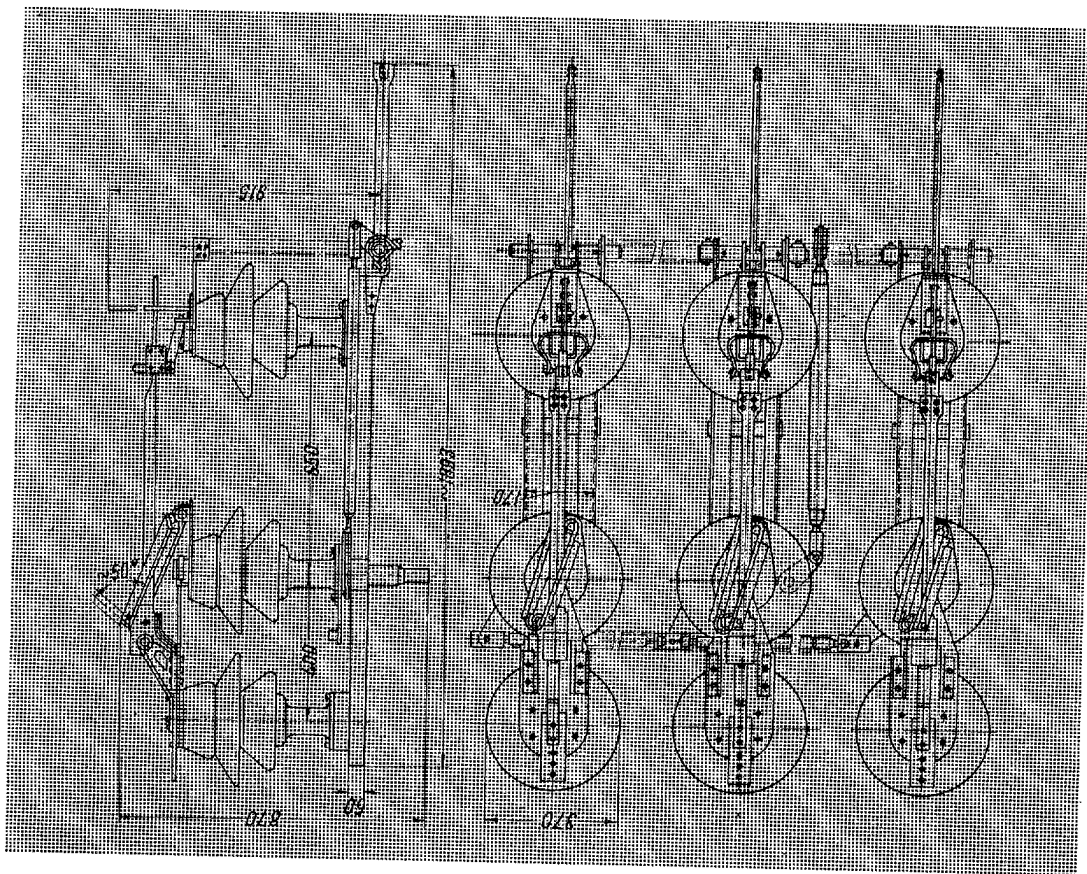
Габаритный эскиз разьединителя РЛНЗ-35.
